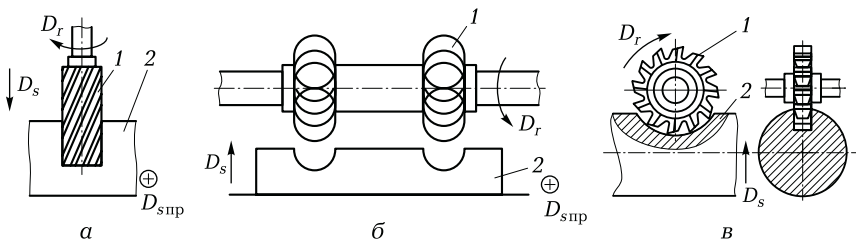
Схемы обработки пазов концевой (а), фасонной (б) и дисковой шпоночной (в) фрезами на фрезерных станках:
